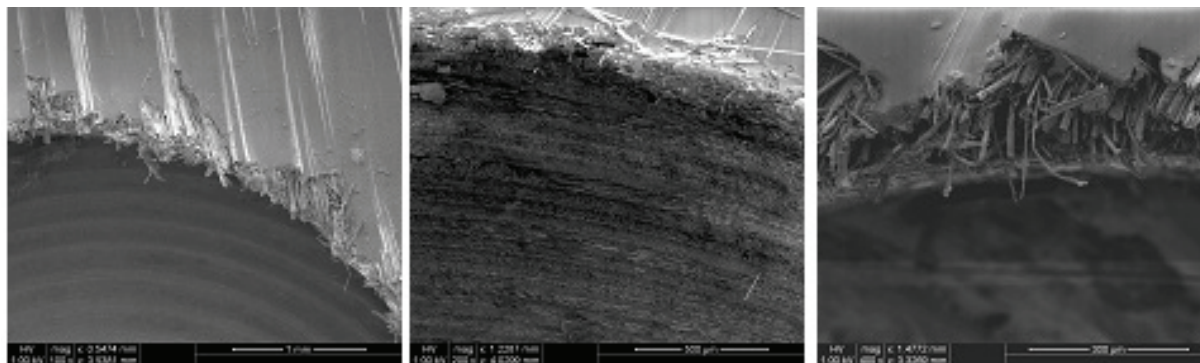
Дефекты на кромках деталей из ПКМ, возникающие при механической обработке -фрезеровании и сверлении
